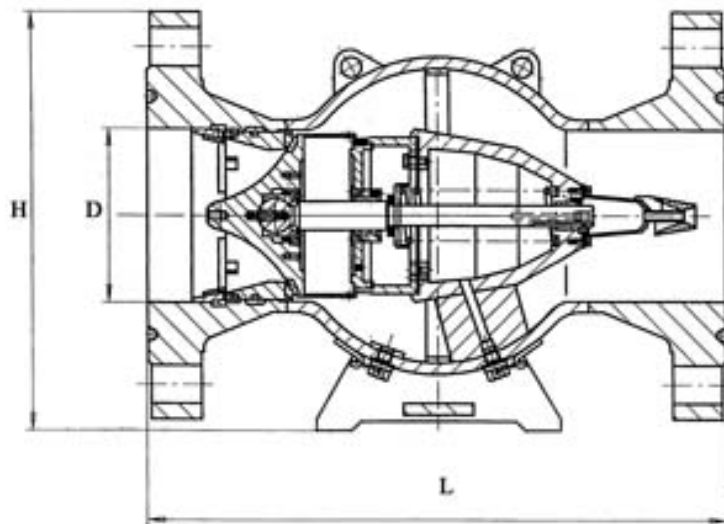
Клапан зворотний безударний K41122-150 під приварювання
